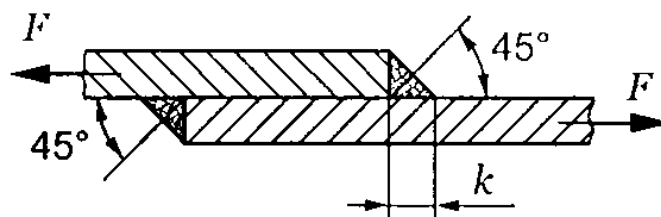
Схема напусків зварних з'єднань кутовими швами.
